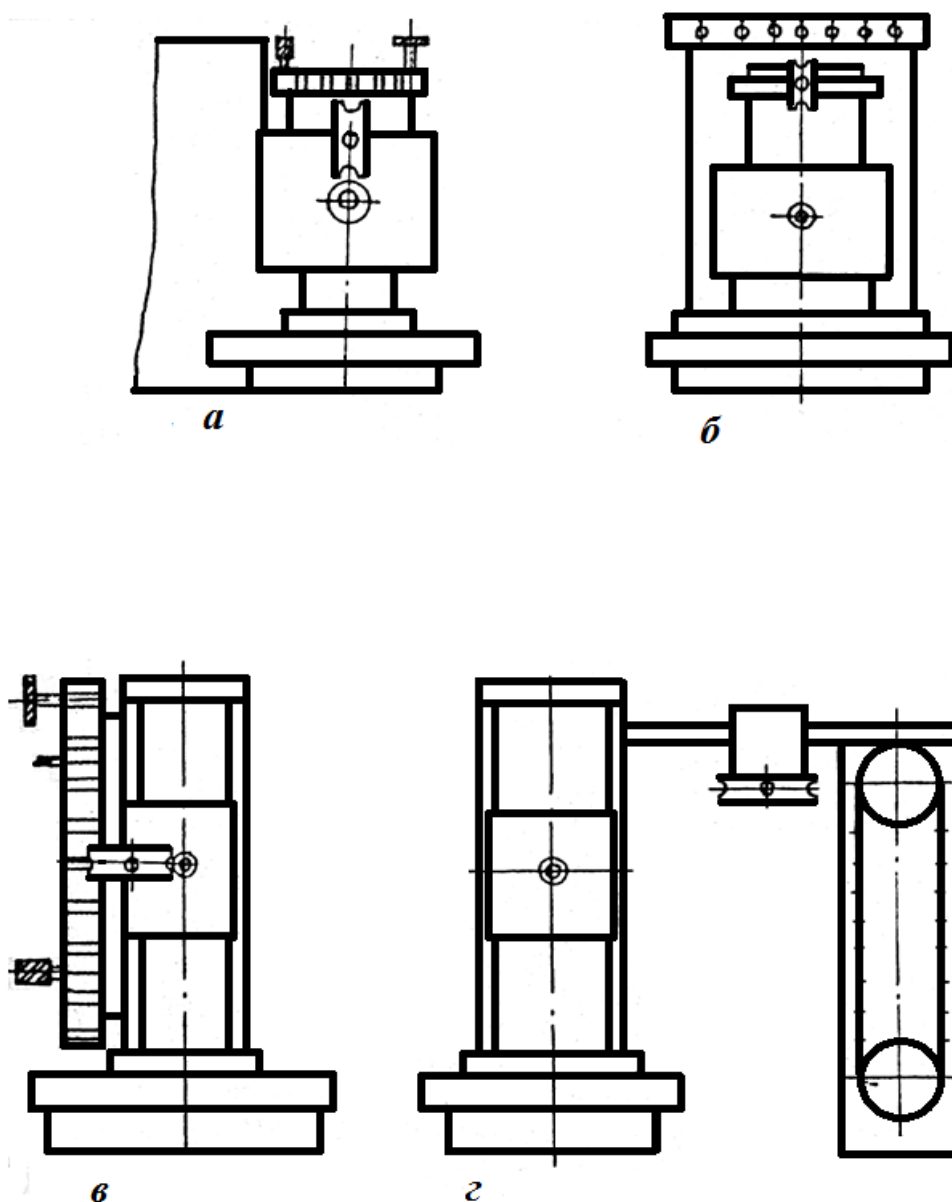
Основні схеми розташування інструментальних магазинів верстатів з ЧПК
